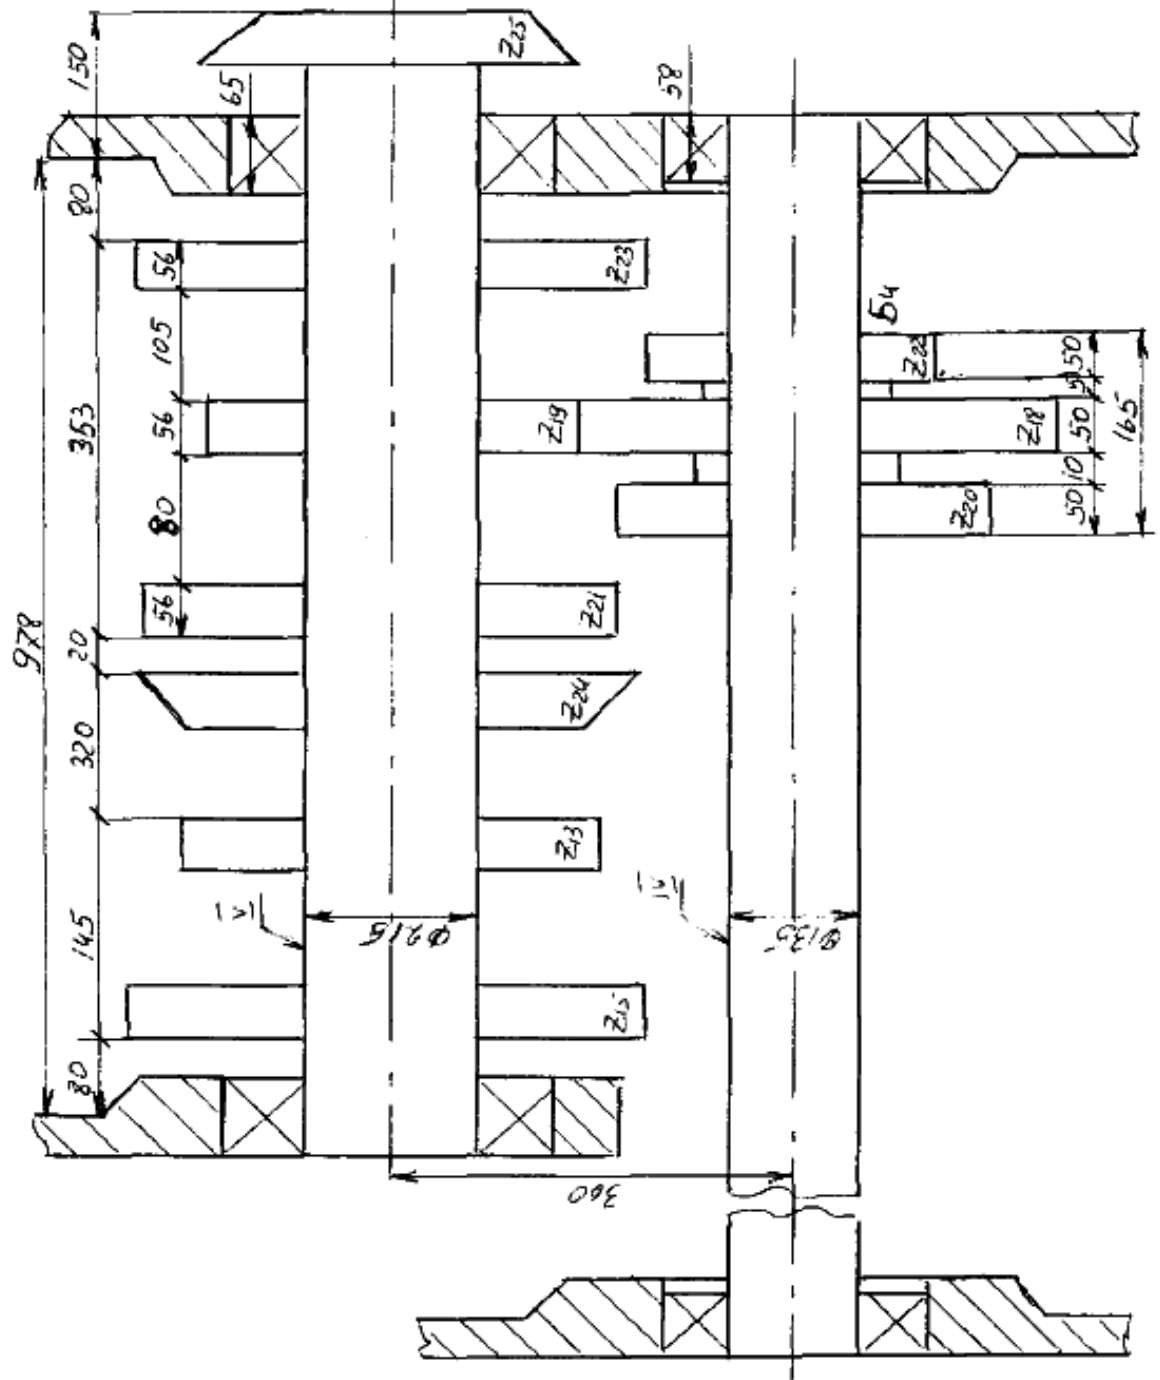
Компоновочная схема развертки наиболее нагруженной группы передач
